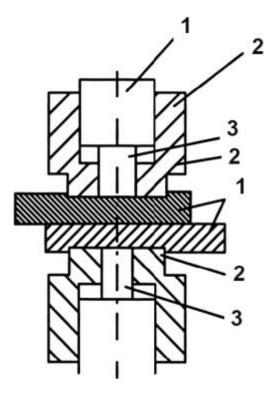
Схема холодной сварки с предварительным зажатием свариваемых деталей:
